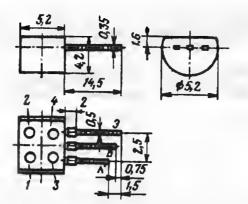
Чертеж корпуса и цоколевка траизисторов серии КТ3107
